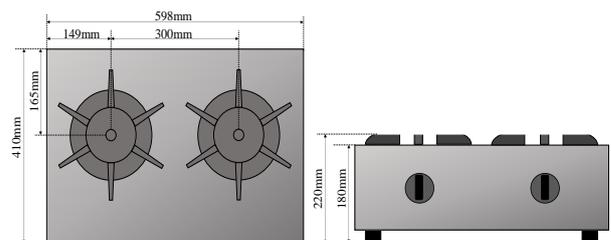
ガスこんろ外形寸法（左: 平面図、右: 立面図）
